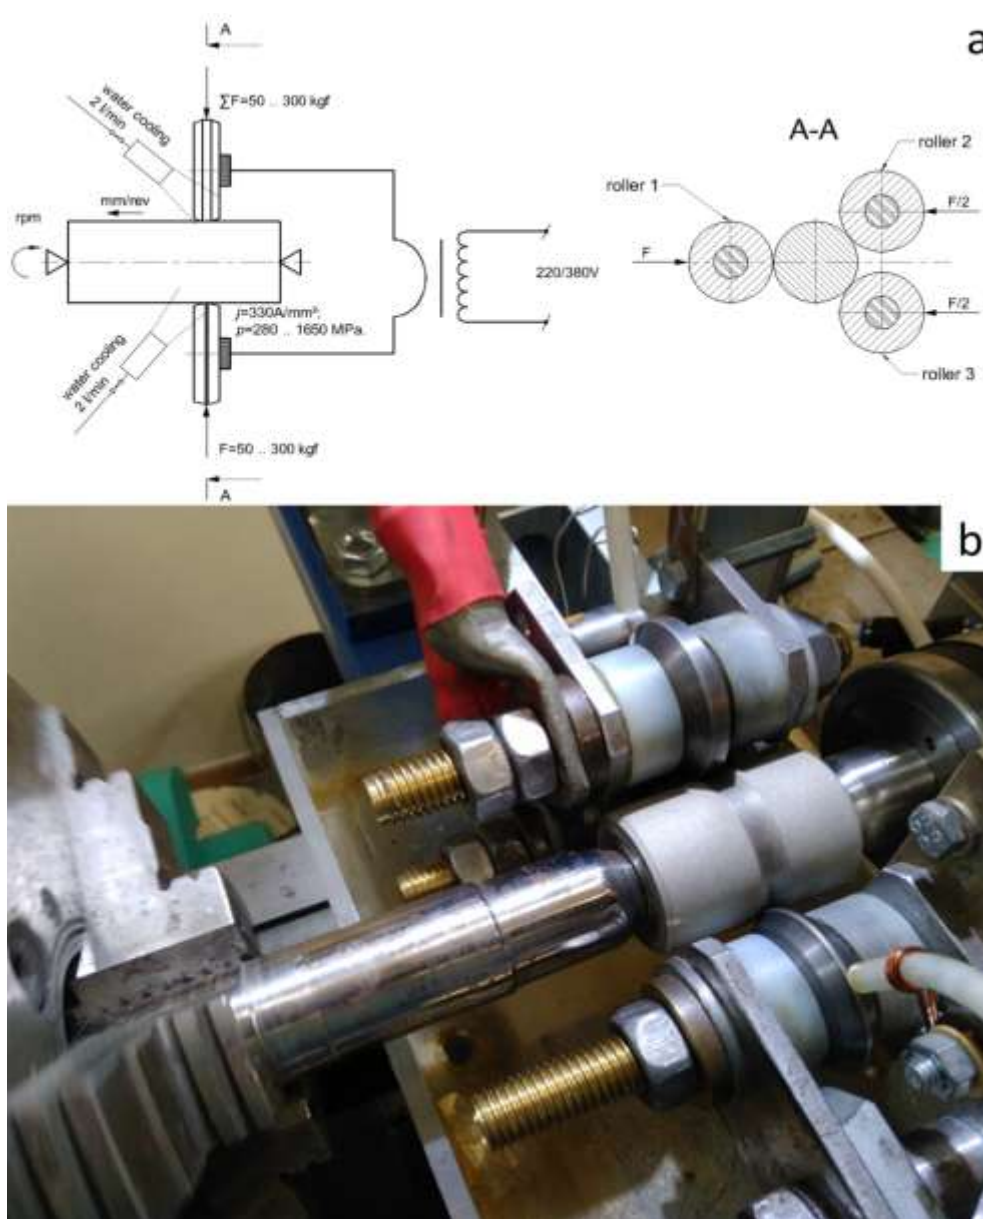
Принципиальная схема электромеханической обработки цилиндрических деталей (а), зона обработки на токарном станке (б)
